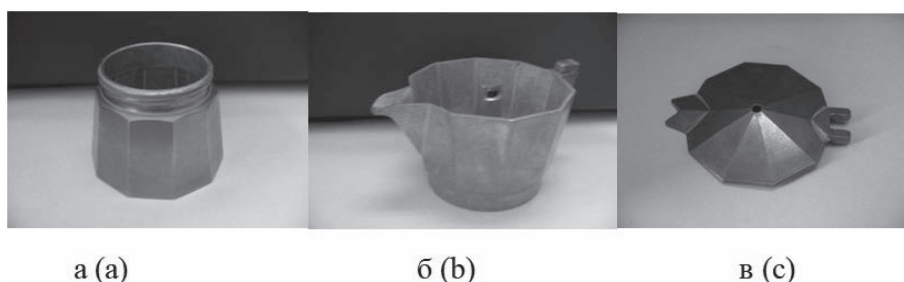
Внешний вид деталей из алюминиевого сплава: а- корпус, б- накопитель, в- крышка
